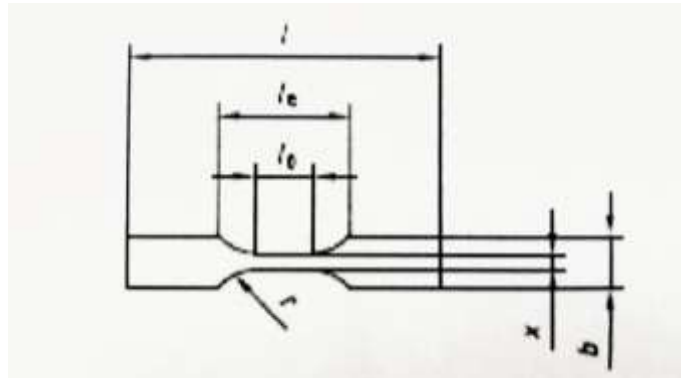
Provete obtido após maquinação com as dimensões recomendadas.
